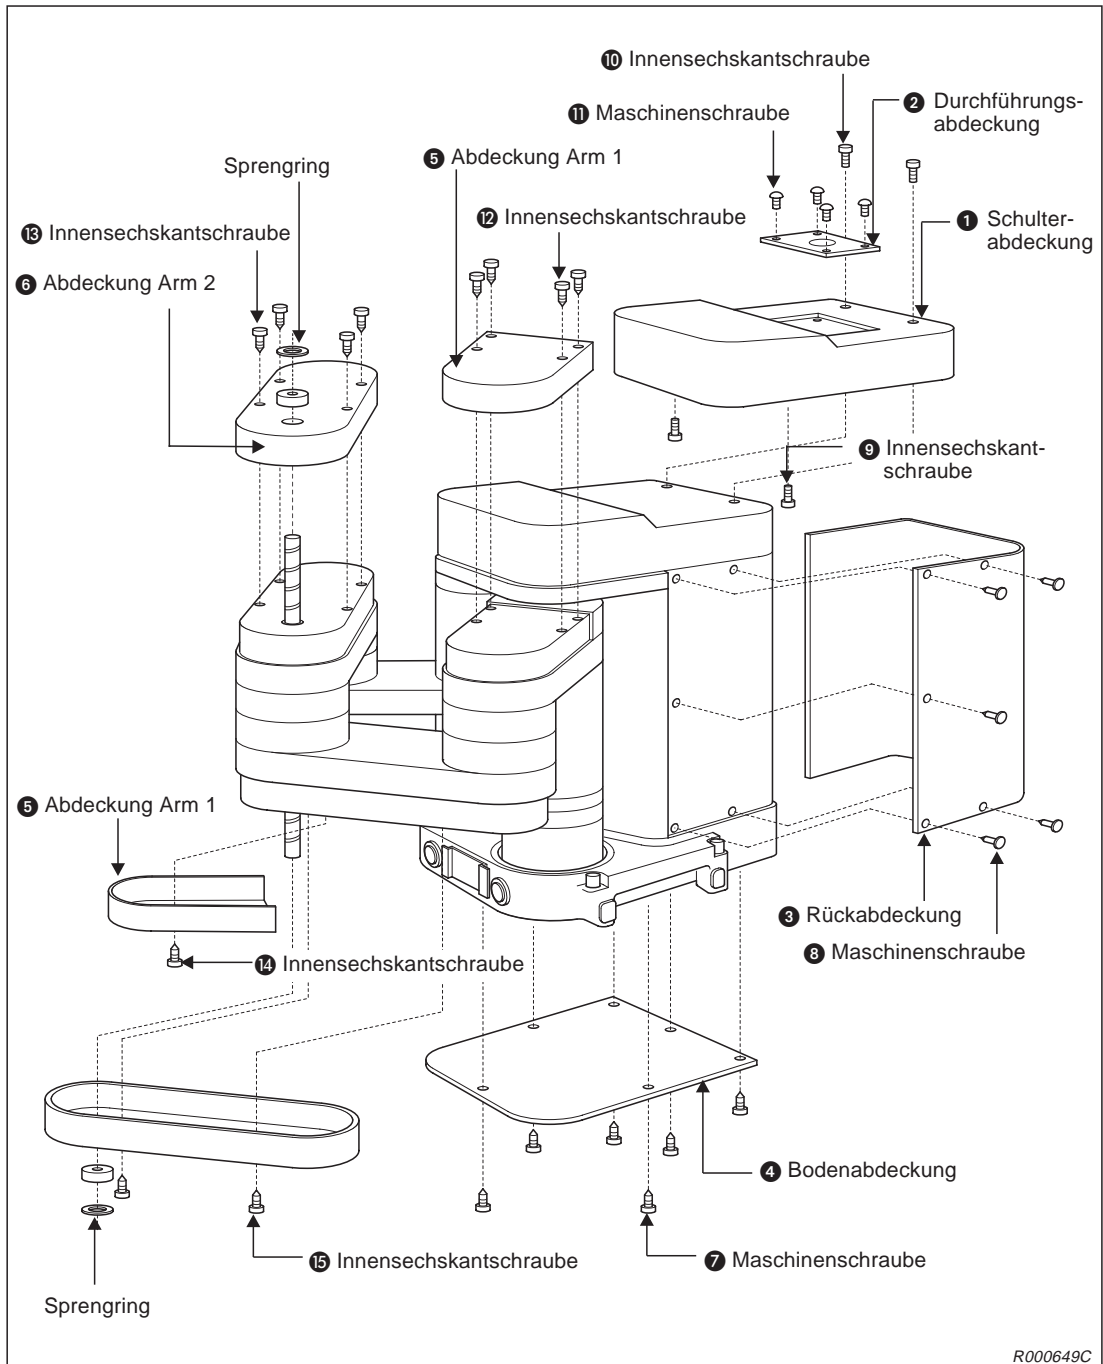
Lage und Bezeichnung der Gehäuseabdeckungen
